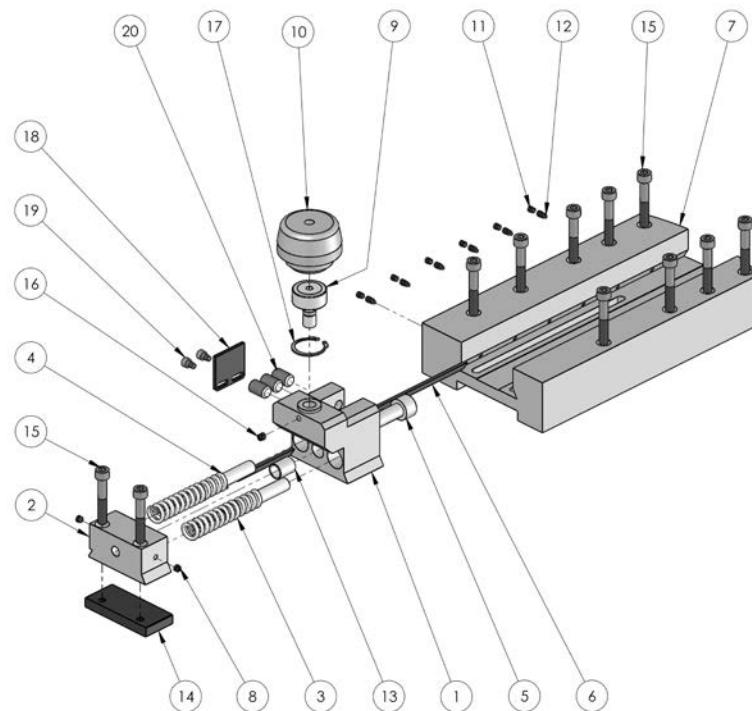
1 – Резцедержатель; 2 – Опорная планка; 3 – Пружина; 4 – Стержень; 5 – Регулировочный винт; 6 – Направляющая скольжения; 7 – Корпус суппорта; 8 – Стопорный винт; 9 – Ролик; 10 – Ролик наружный; 11 – Стопорный винт; 12 – Стопорный винт; 13 – Направляющее кольцо; 14 – Нижняя опорная планка; 15 – Винт; 16 – Винт стопорный; 17 – Стопорное кольцо; 18 – Стружкоотделитель; 19 – Винт; 20 – Винт стопорный
